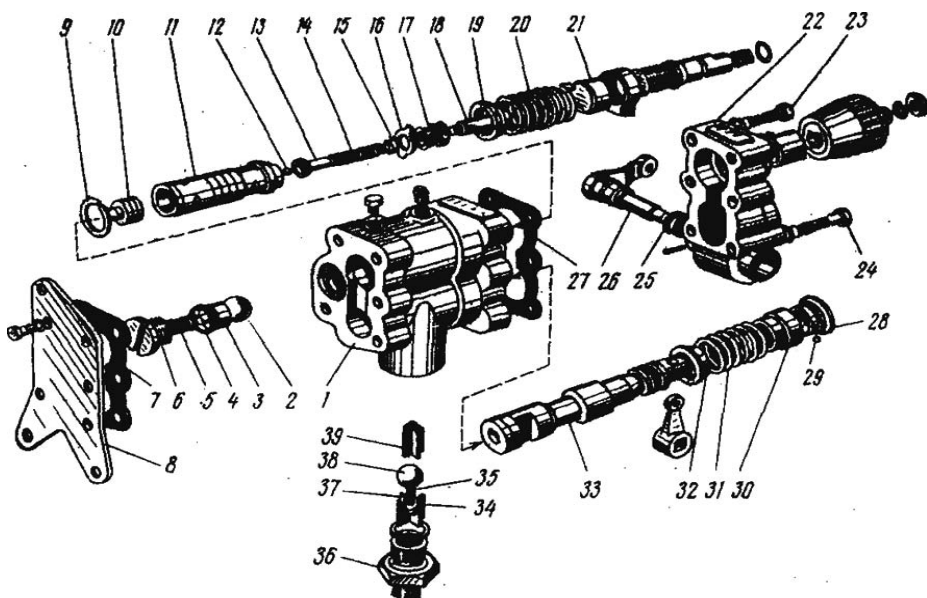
Разборка ГСВ. 1 — корпус гидроувеличителя в сборе; 2, 12, 29 и 38 — шарики; 3 — направляющая обратного клапана; 4 и 25 — уплотнительные кольца; 5 — пружина всасывающего клапана; 6 — пробка; 7 — задняя прокладка; 8 — задняя крышка; 9 — кольцо; 10 — большой плунжер; 11 — золотник; 13 — направляющая предохранительного клапана; 14 — пружина предохранительного клапана; 15 — упорная шайба; 16 — стопорная шайба; 17 — гайка; 18 — малый плунжер; 19 — упор пружины; 20, 31 и 35 — пружины; 21 — колпак; 22 — передняя крышка; 23 и 24 — болты; 26 — рычаг с осью в сборе; 27 — передняя прокладка; 28 — сепаратор; 30 — обойма фиксатора; 32 — стакан; 33 — ползун; 34 — верхняя крестовина; 36 — штуцер; 37 — нижняя крестовина; 39 — толкатель
